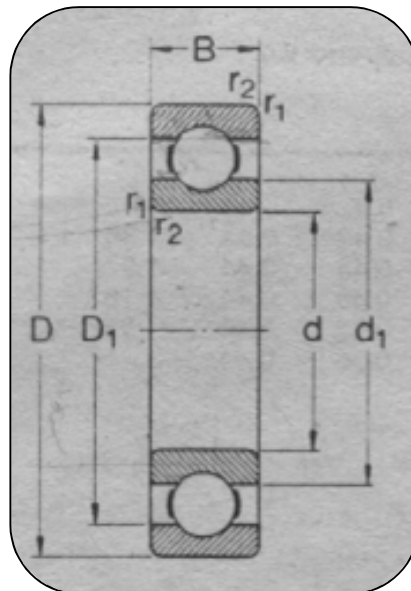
Dimensión del rodamiento de bolas ⁽⁶⁾.
